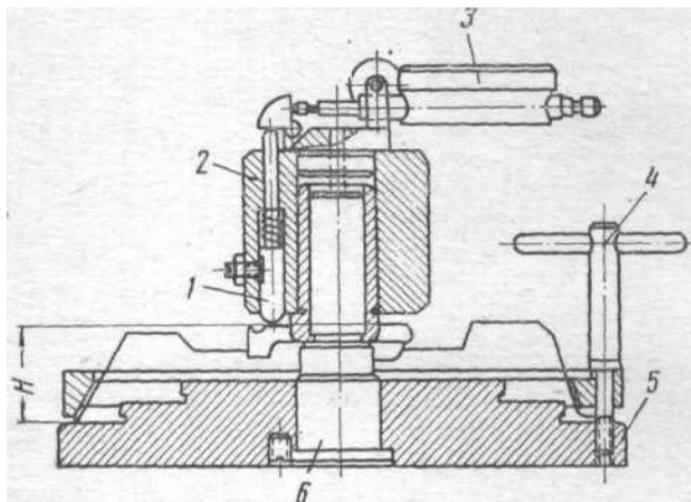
Приспособление для проверки биения пяты рычагов выключения сцепления:
